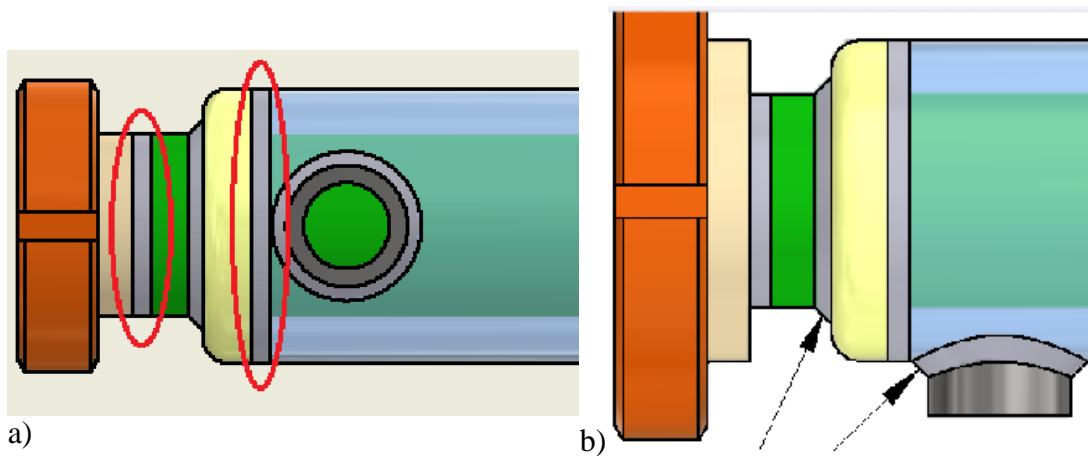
a) Junta a tope para soldadura autógena CJP y b) junta en esquina para soldadura de filete PJP.
